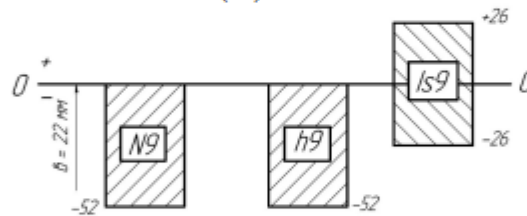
Схема розташування полів допусків деталей шпонкового з'єднання по ширині b
